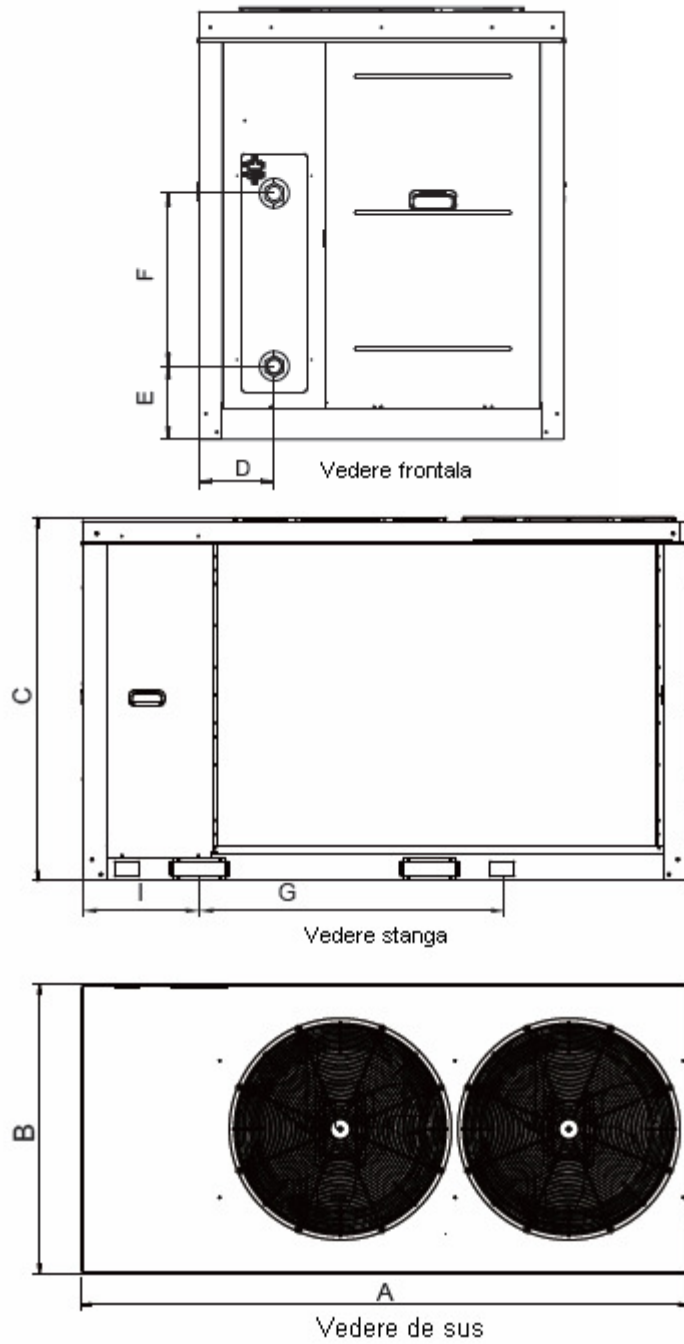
| Desene dimensionale MC-SU60-RN1L
